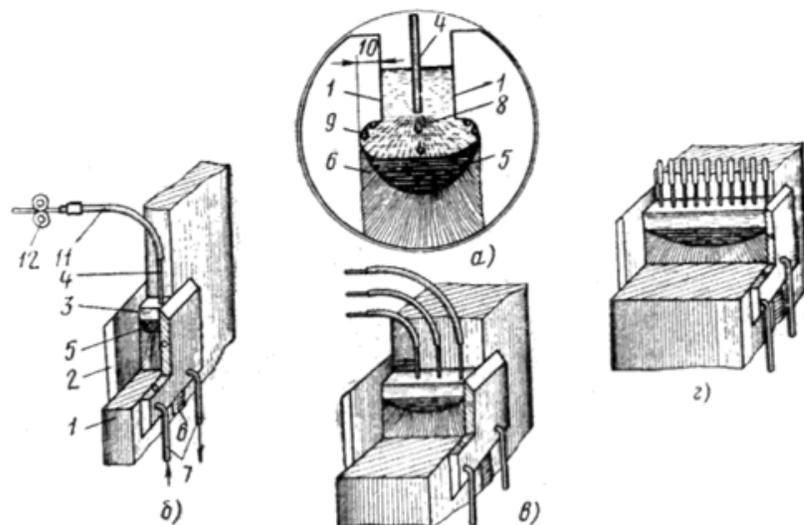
Схема процесса электрошлаковой сварки: *а* — принципиальная схема; *б* — сварка одним электродом с неподвижной осью; *в* — сварка тремя электродами, имеющими возвратно-поступательное движение; *г* — многоэлектродная сварка; 1 — свариваемый металл; 2 — медные ползуны, охлаждаемые водой; 3 — шлаковая ванна; 4 — электродная проволока; 5 — металлическая ванна; 6 — сварной шов; 7 — трубки для подвода и отвода воды; 8 — капли плавящегося электрода; 9 — капли оплавленного металла; 10 — величина проплавления кромок металла; 11 — токоподводящий мундштук; 12 — ролики, подающие проволоку в шлаковую ванну
